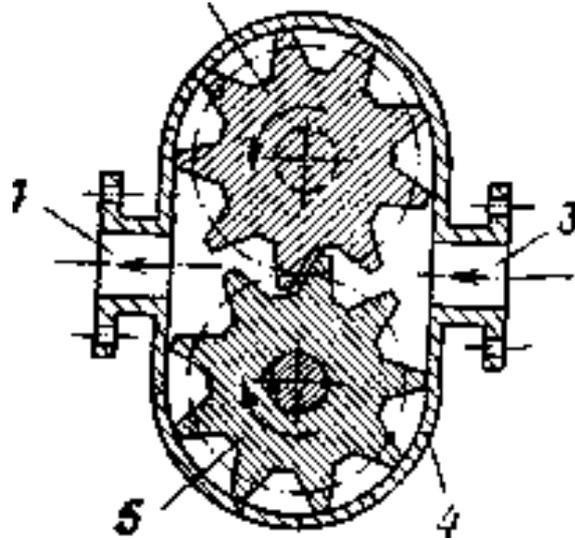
Схема шестеренного насоса: 1 – напорная полость; 2 – ведомая шестерня; 3 – всасывающая полость; 4 – корпус; 5 – ведущая шестерня
